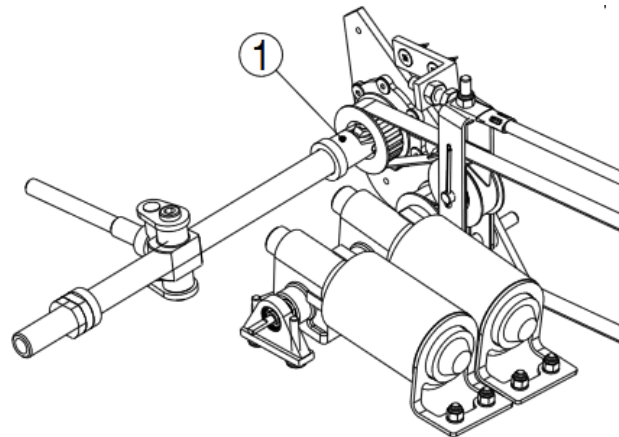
Vue 3D du système de commande de volet QPL2800 / Flap Control System QPL2800 3D View
